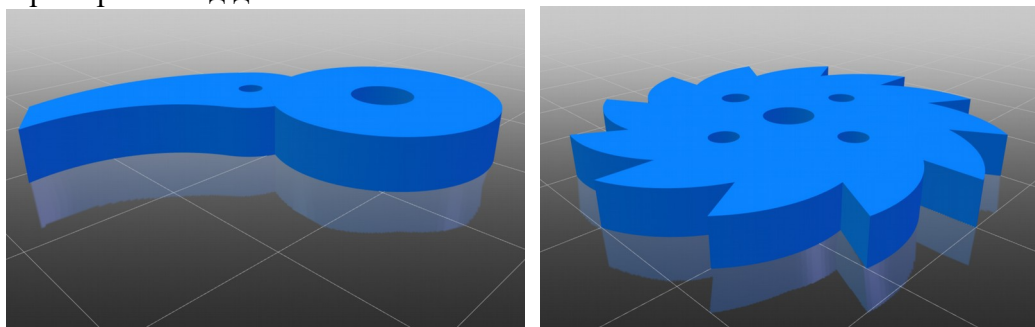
Схема храпового механизма: Собачка (a) и зубчатое колесо (b)
